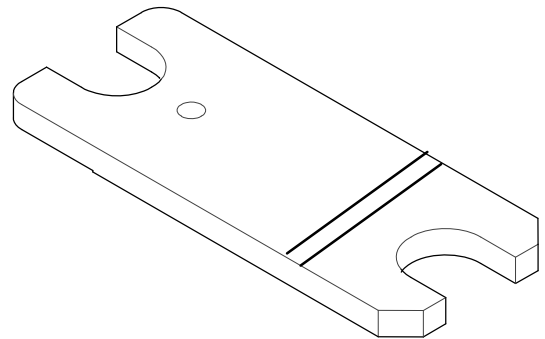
Galga de inspección de montaje de dos lados para racores instalados manualmente
